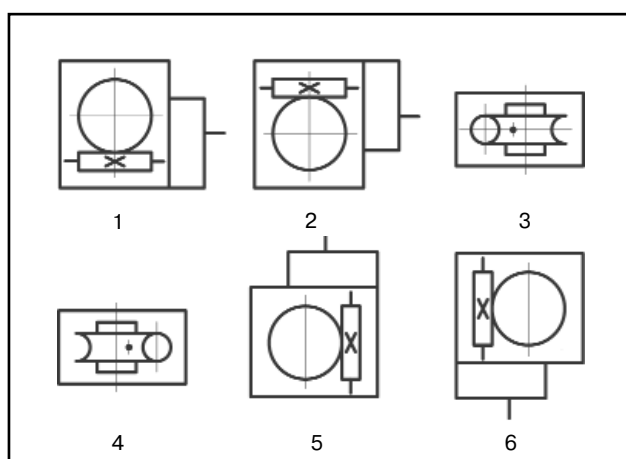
Варианты расположения червячных передач редукторов типа ЦЧ:
